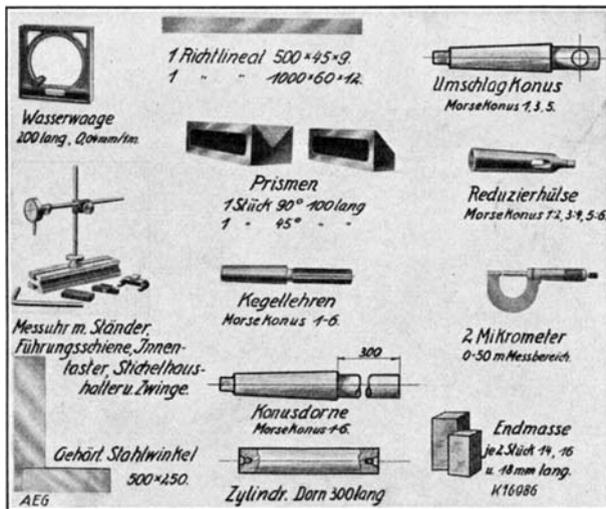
Satz Revisionswerkzeuge für Werkzeugmaschinen.
